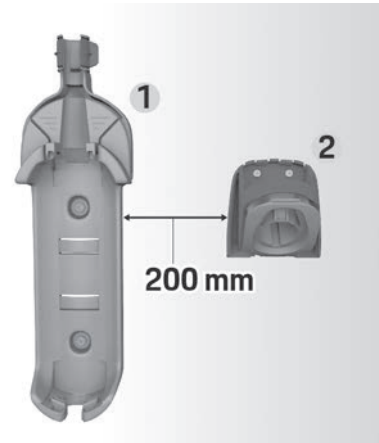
Abstand Wandhalterung – Steckerhalterung
